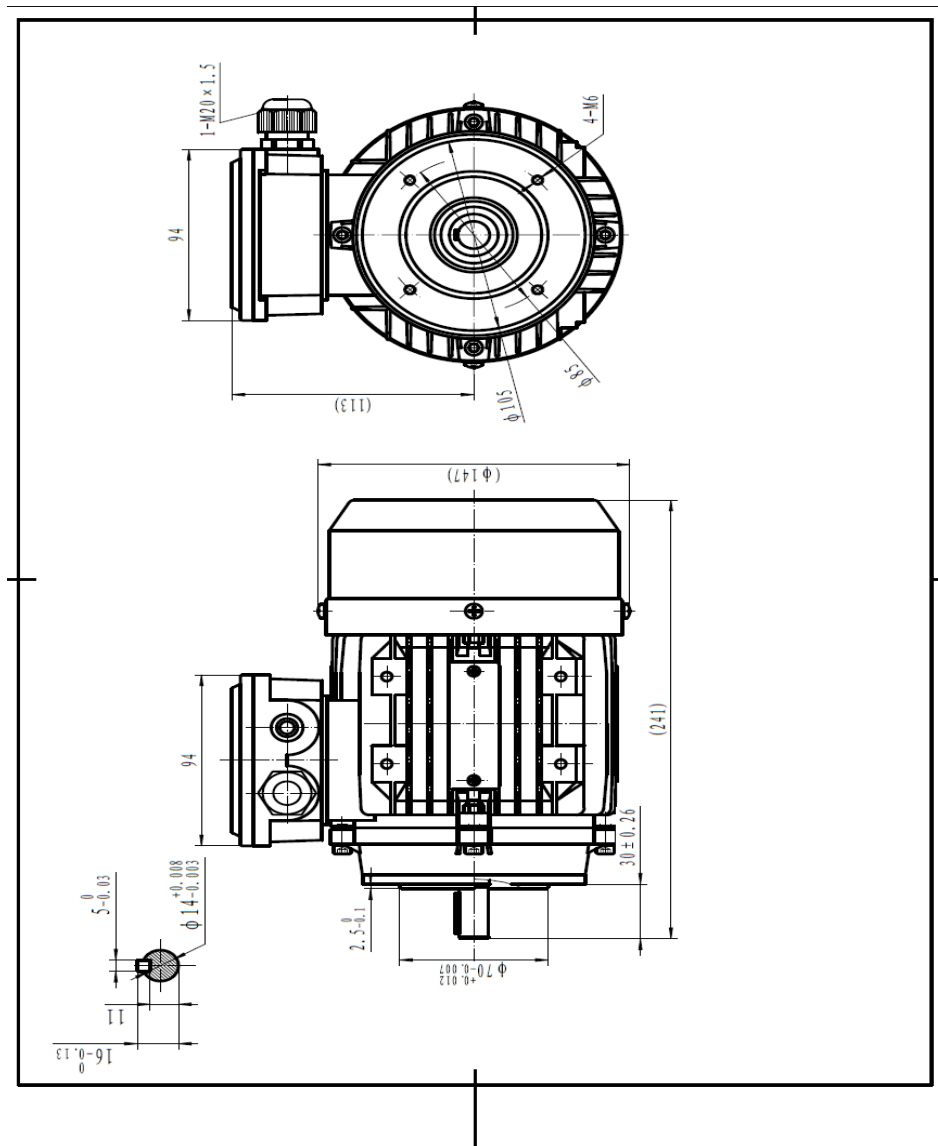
Dibujo técnico del motor eléctrico. <sup>[18]</sup>
